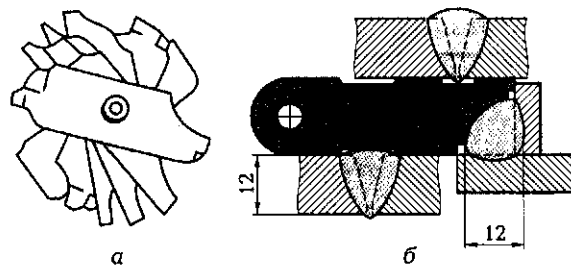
Универсальный шаблон для контроля угловых швов (а) и специальный шаблон для контроля сварных швов (б)
